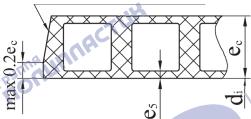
Схема снятия фасок с кромки трубы для соединения экструзионной сваркой с проведением сварочных работ снаружи трубы
